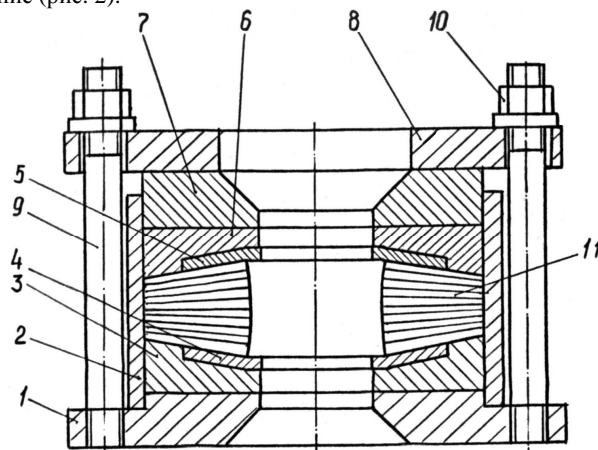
Приспособление для сборки цилиндрической иглофрезы
